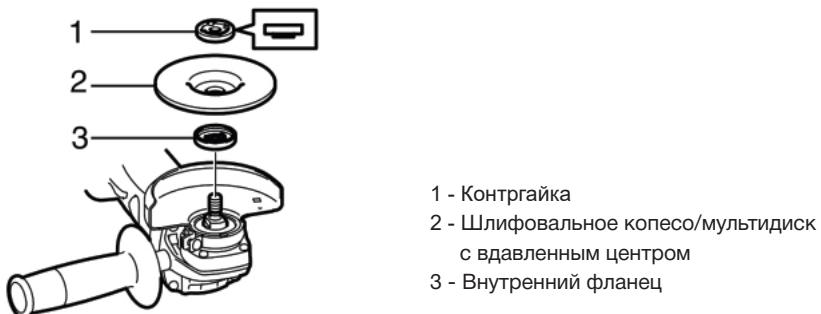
Установка рабочего диска для аккумуляторной угловой шлифовальной машине серии DLAG.
